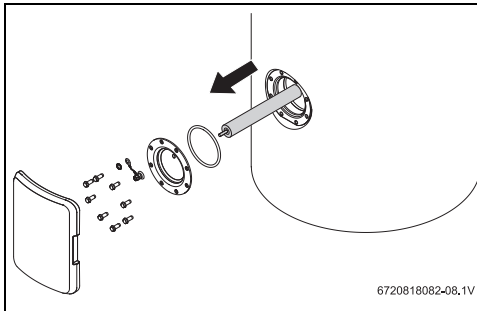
Kontrolle des Zustands der Magnesium-Anode
